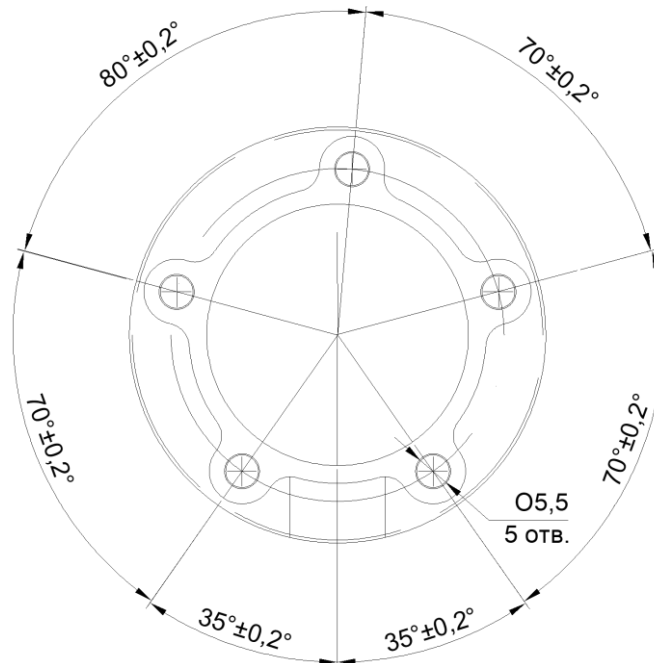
Схема расположения отверстий под крепежные элементы
